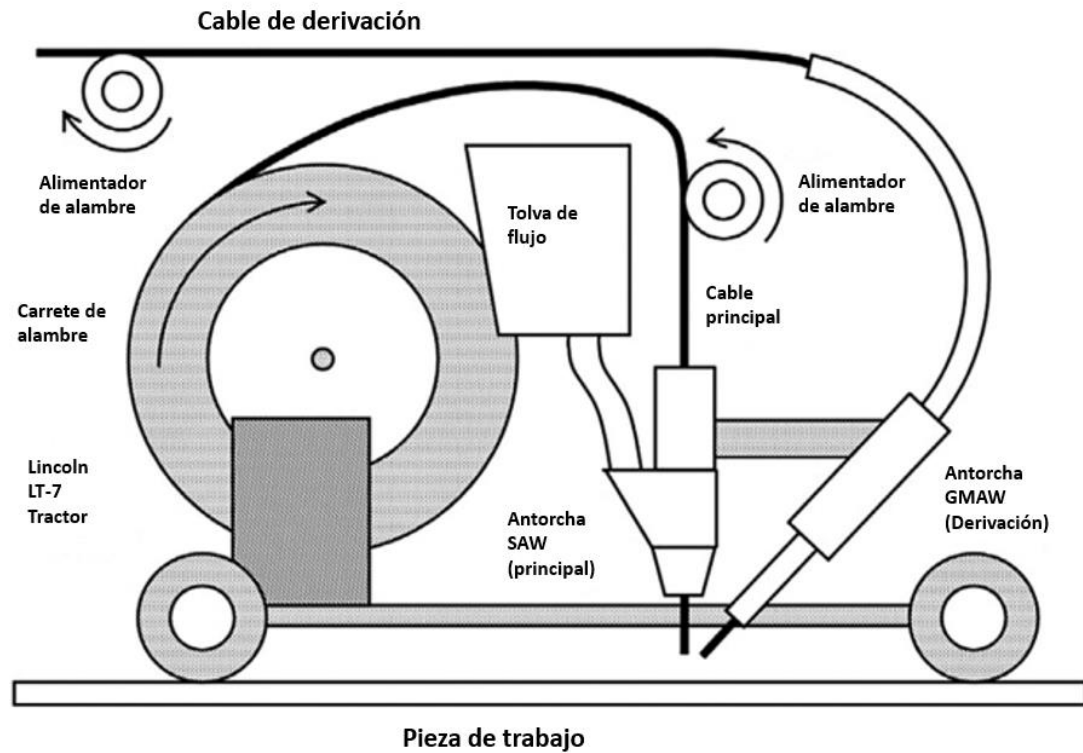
Soldadura híbrida SAW-GMAW. Modificado de (Lu y col., 2014).
